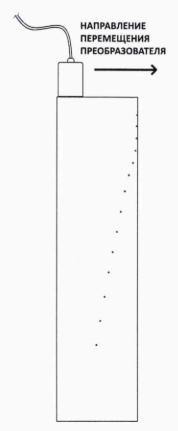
Положение преобразователя на поверхности меры МД 2-0-1
